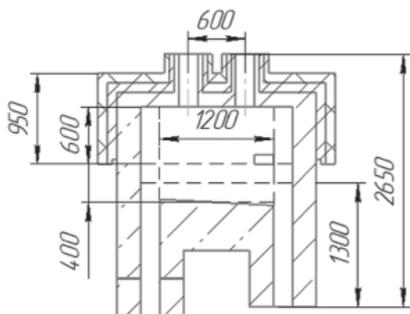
Эскизный чертёж вакуум-камеры непрерывного действия П-образного типа
